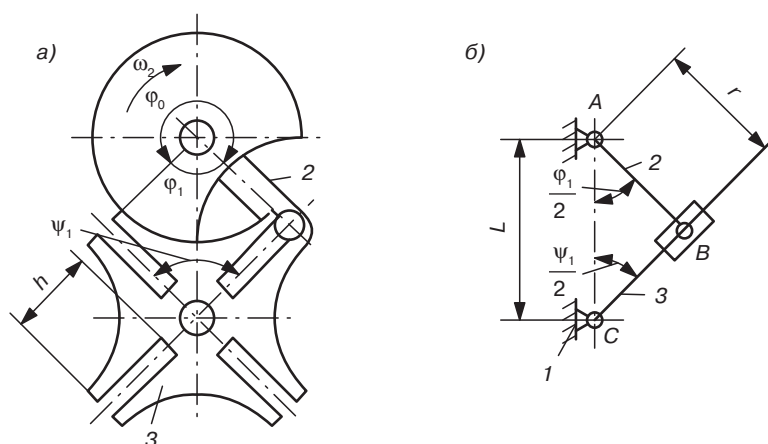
Схема мальтийского механизма с внешним зацеплением: а — схема; б — эквивалентный кривошипно-кулисный механизм; 1 — стойка; 2 — кривошип; 3 — крест
